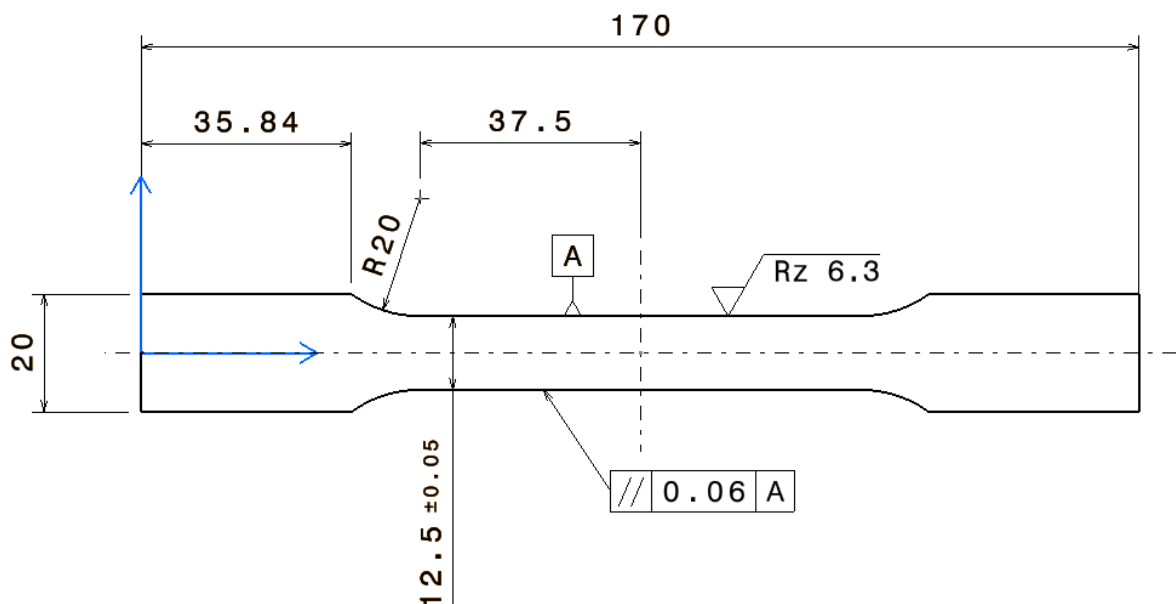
Zugprobe der Form H gemäß DIN50125.
